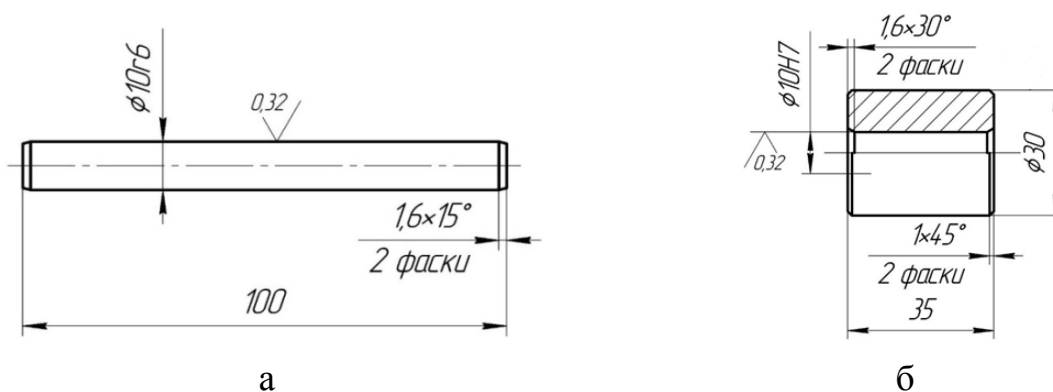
Конструкция образцов деталей соединения с натягом:
